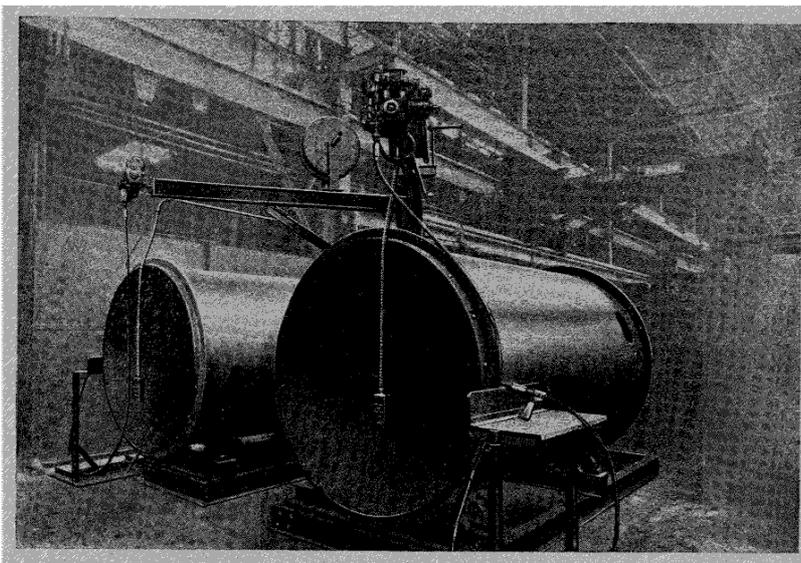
Machine semi-automatique pour la soudure circulaire des fonds de réservoirs.
